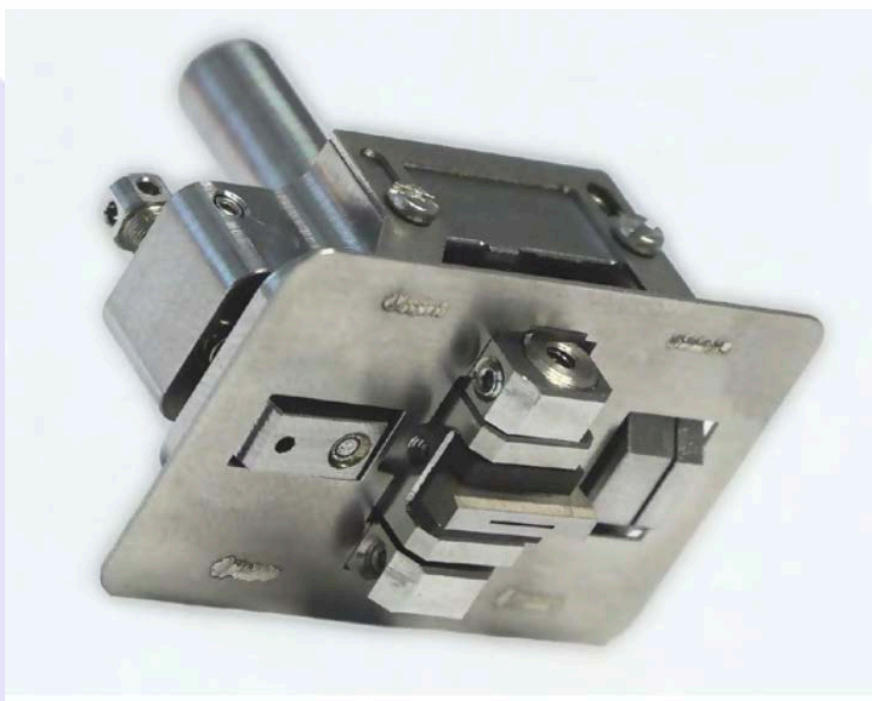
Инструмент для пайки лазерного диода пружинной конструкции
